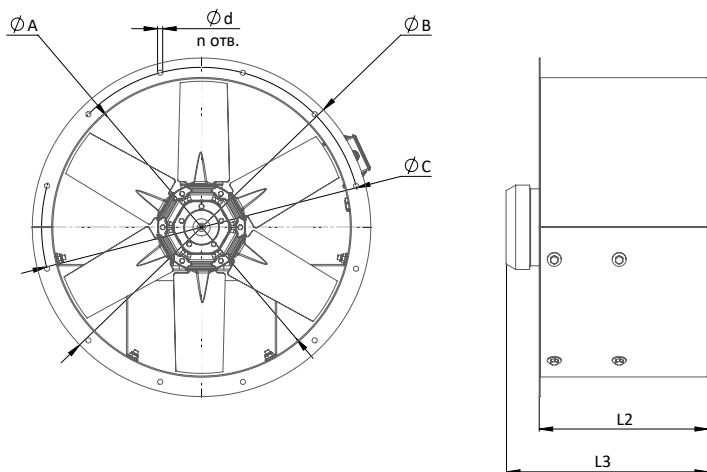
Габаритные размеры вентилятора в исполнении корпуса «HS»
